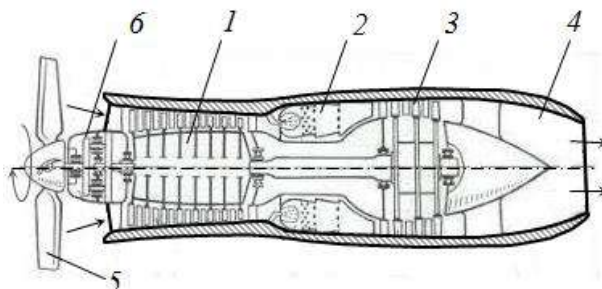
Схема турбогвинтового двигуна: 1 – компресор; 2 – камера згоряння; 3 – газова турбіна; 4 – сопло; 5 – гвинт; 6 – редуктор
